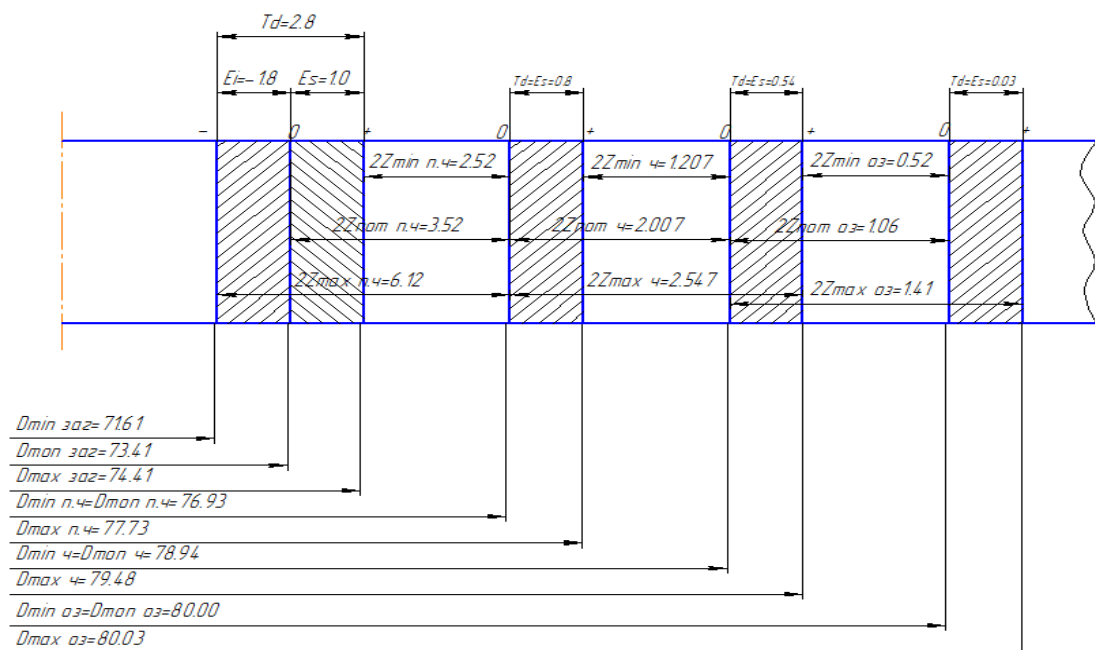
Схема розташування припусків і допусків для поверхні Ø80H7
